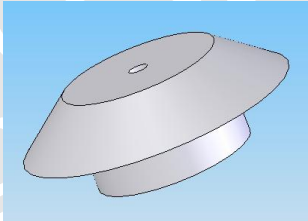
Assembly komponen pompa toothpaste dispenser
